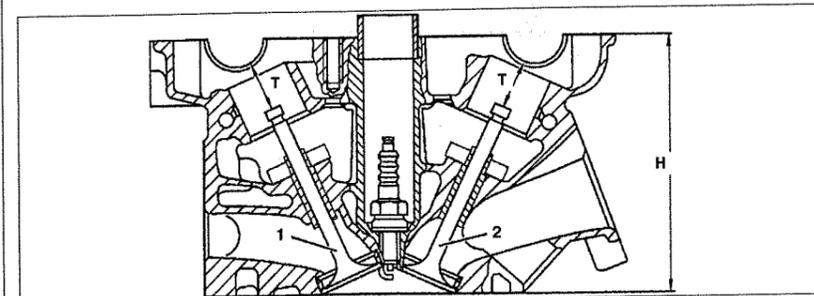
Проверка расстояния от кончика стержня клапана до подшипника распределительного вала.
